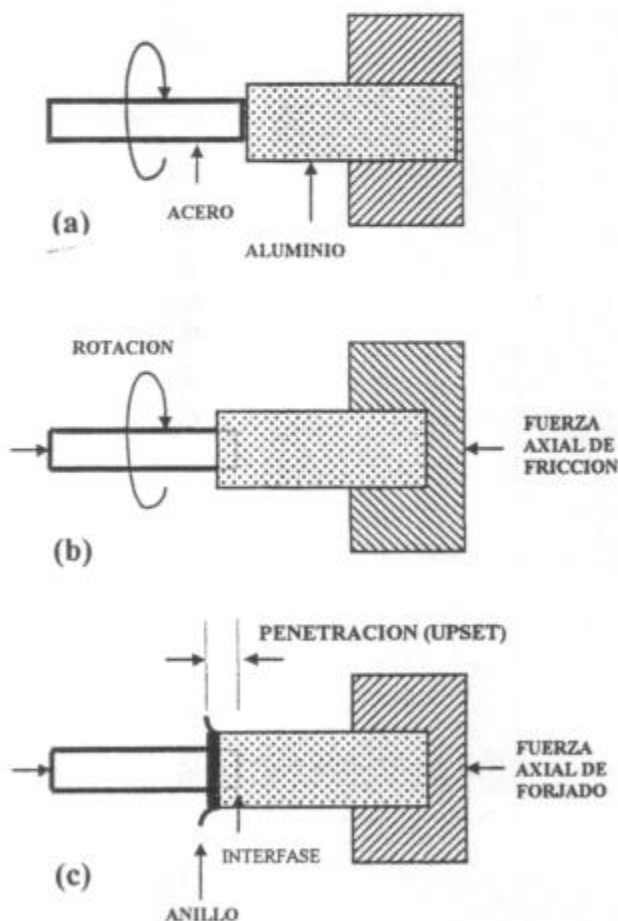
Proceso de soldadura por fricción convencional.
